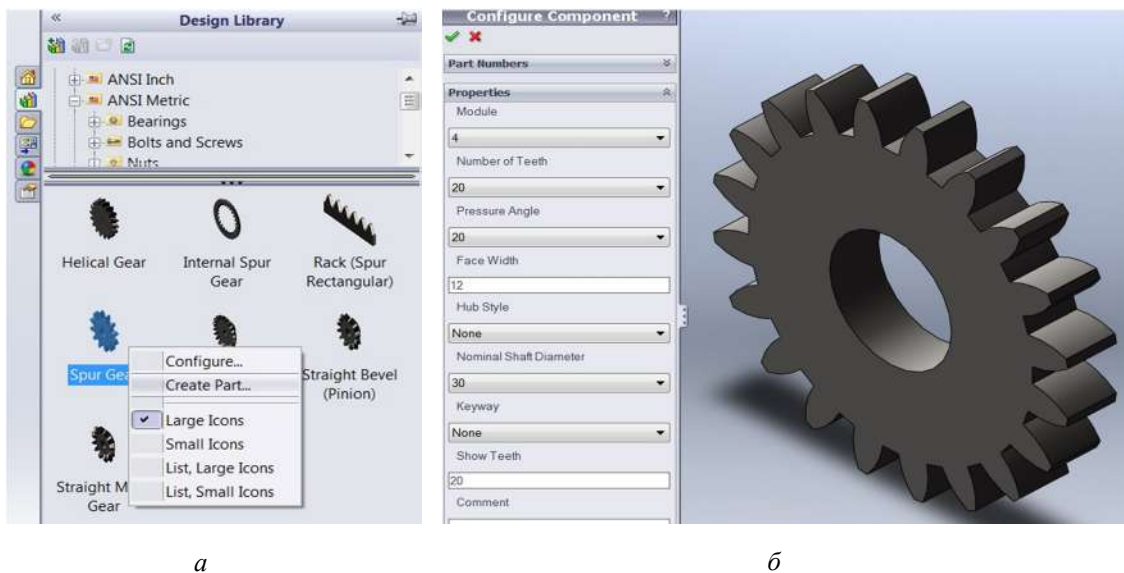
Створення зубчастого колеса з використанням Toolbox:
